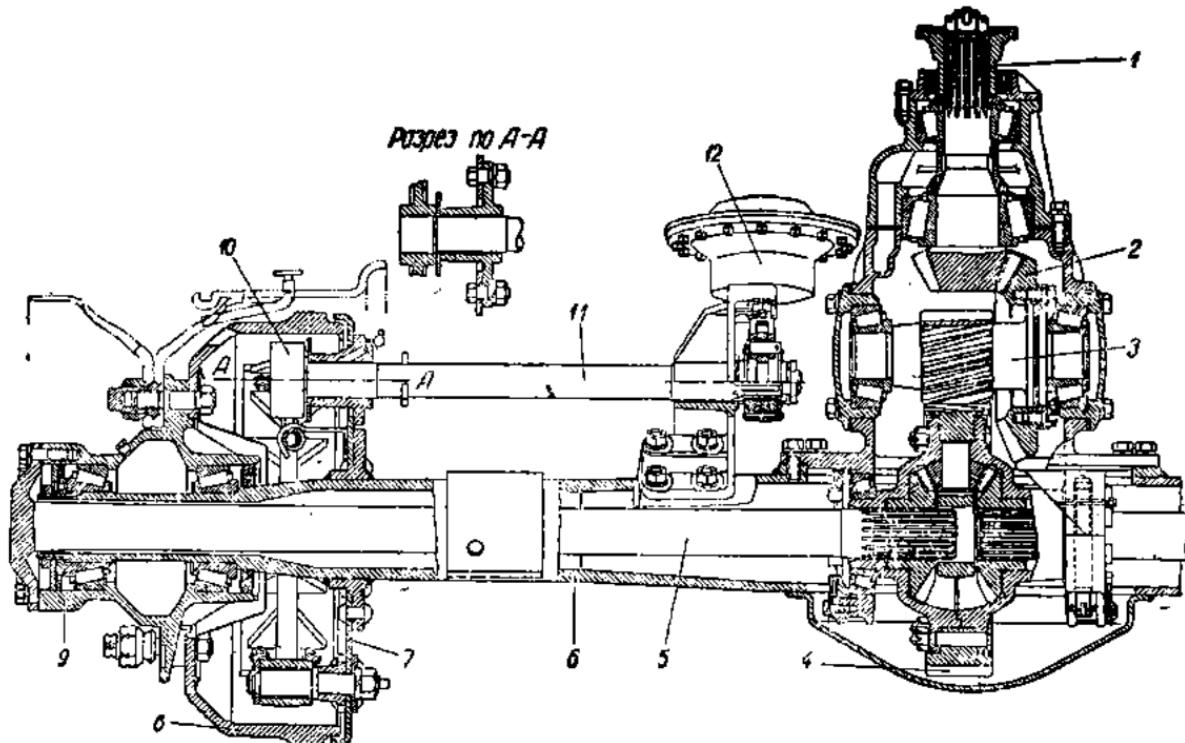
Задний мост и главная передача. (1 — ведущая шестерня редуктора; 2 — ведомая шестерня редуктора; 3 — промежуточный вал и ведущая шестерня главной передачи; 4 — ведомая шестерня главной передачи; 5 — полуось; 6 — кожух полуоси; 7 — опорный тормозной диск; 8 — тормозной барабан; 9 — ступица; 10 — разжимной кулак колодок; 11 — тормозной вал; 12 — тормозная камера).
